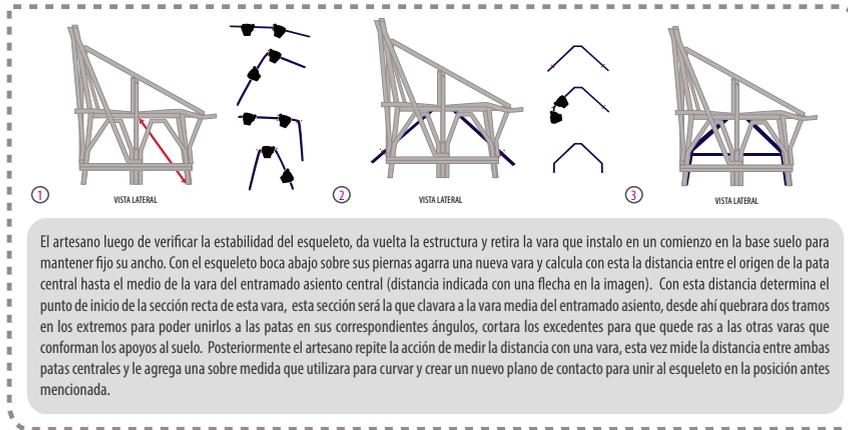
Imagen X Construcción varas centrales inferiores, Elaboración propia.
